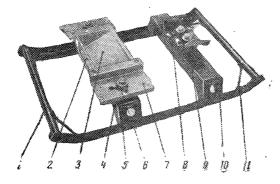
Рама: 1 — каркас; 2 — отверстие короба; 3 — короб; 4 — шпилька с барашком для присоединения провода заземления; 5 — поперечная балка; 6 — гибкий проводник, соединяющий электрически опору с поперечной балкой; 7 — опора для крепления двигателя; 8 опора для крепления генератора; 9— амортизатор; 10— по-перечная балка; 11— распорка
